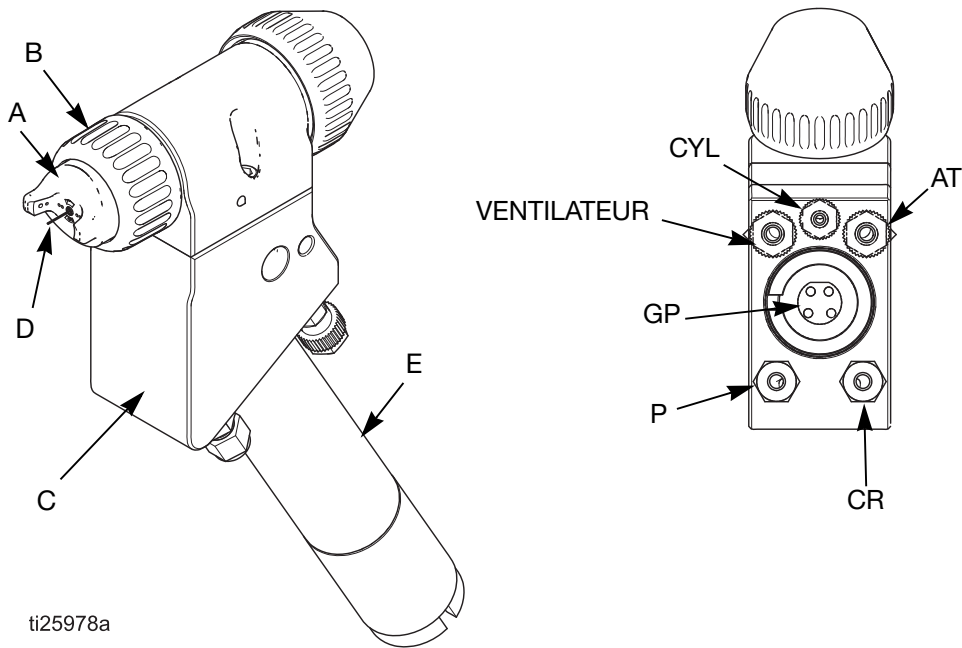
Vue d'ensemble du pistolet (montage par le bas)
